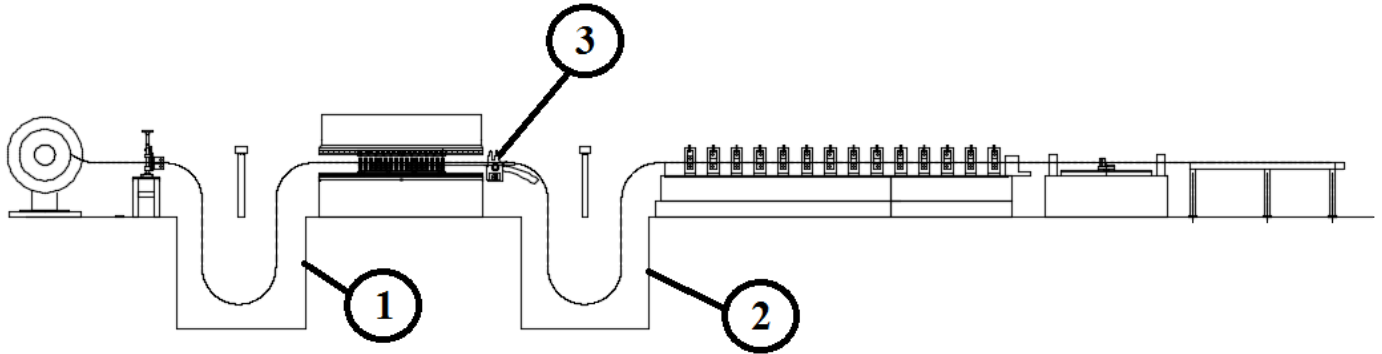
Vista alzado de nuevo layout de máquina. [Elaboración propia, 2019]
